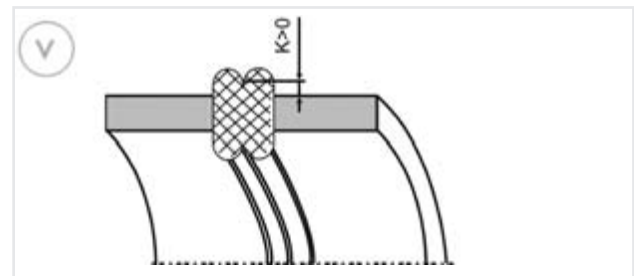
Vue en coupe d'un bon cordon de soudure
